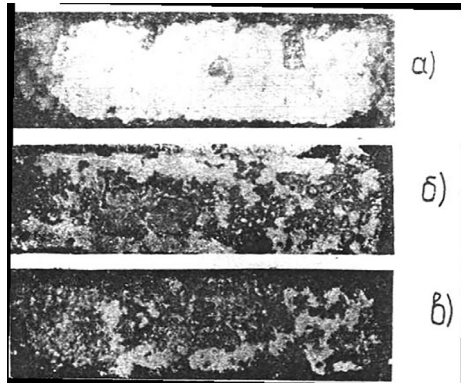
Образцы, наплавленные различными флюсами: а – АСМ; б – ЦСМ; в – ЗОР
